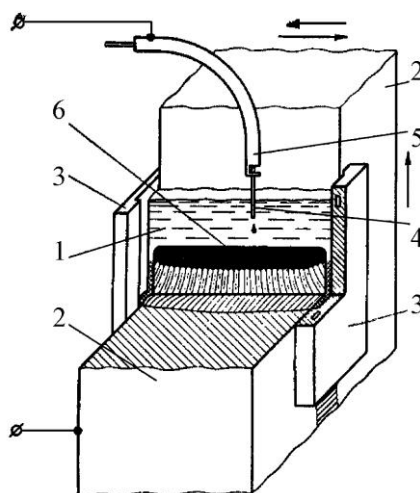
Схема электрошлаковой сварки: 1 – шлак, 2 – заготовки, 3 – водоохлаждающие ползуны, 4 – сварочная проволока (электрод), 5 – мундштук, 6 – сварочная ванна
